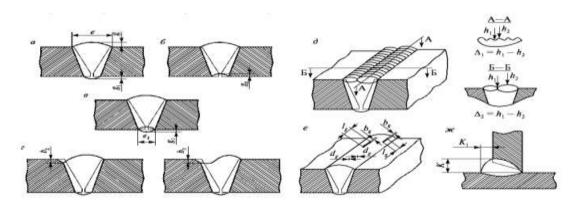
Конструктивные элементы и дефекты сварного шва, подлежащие измерительному контролю
